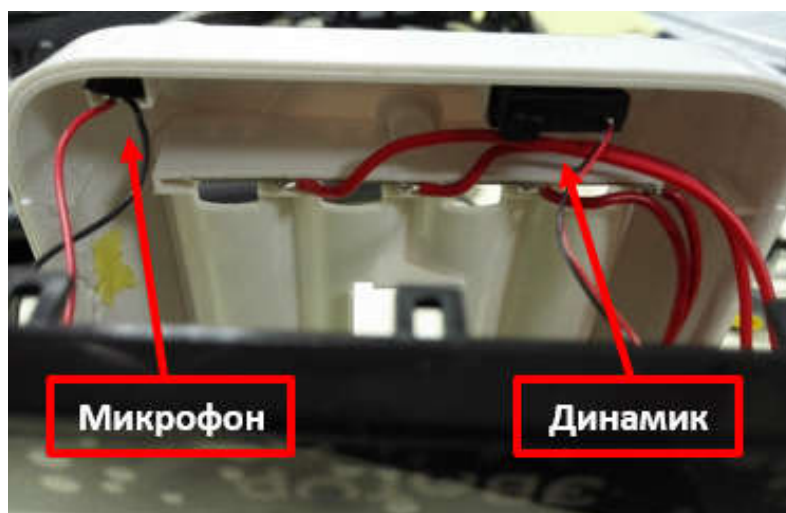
Демонтаж микрофона и динамика из корпуса СТ.
